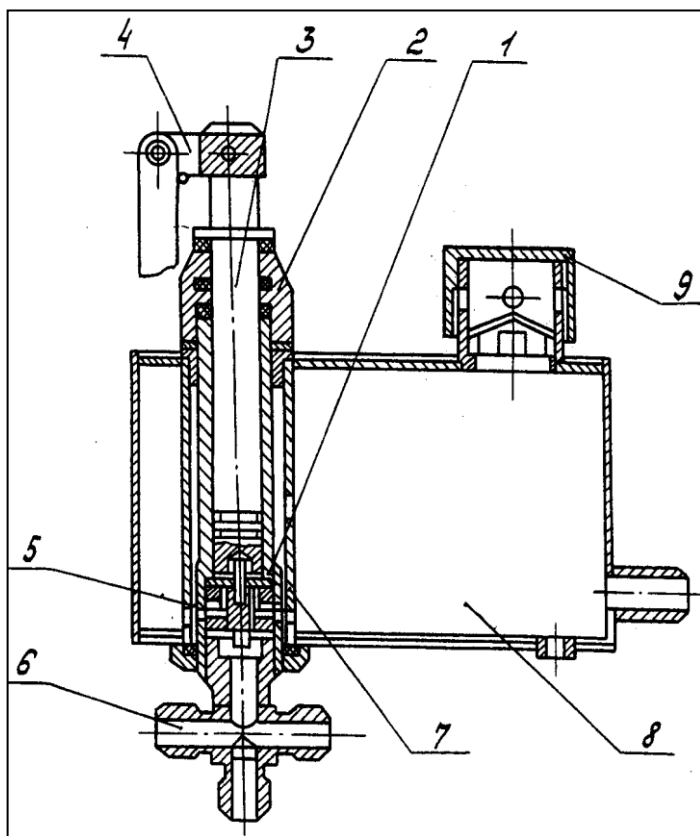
Насос: 1 – корпус; 2 – поджимная гайка; 3 – плунжер; 4 – ручка; 5 – перепускной клапан; 6 – тройник; 7 – гильза; 8 – ёмкость; 9 – заливная горловина
